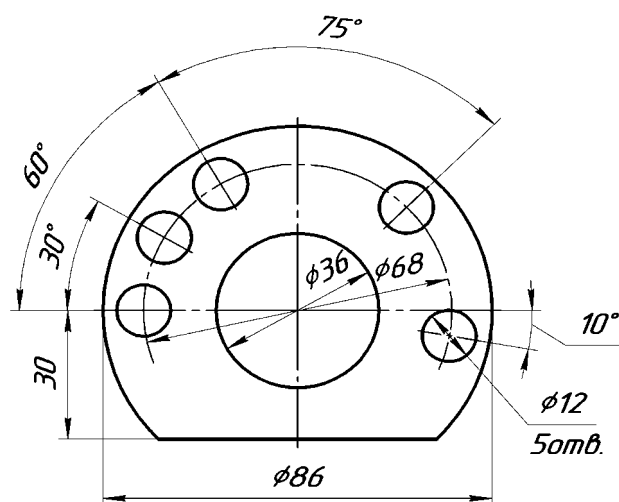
Пример нанесения размеров детали «Фланец»
